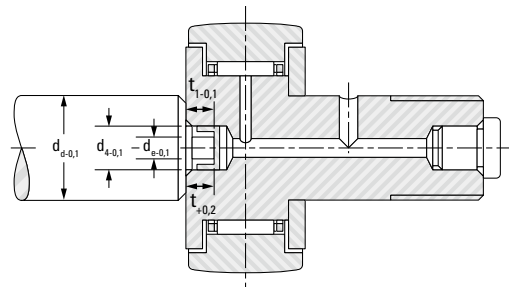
Montagewerkzeug für Stopfen in metrischer Bauform
